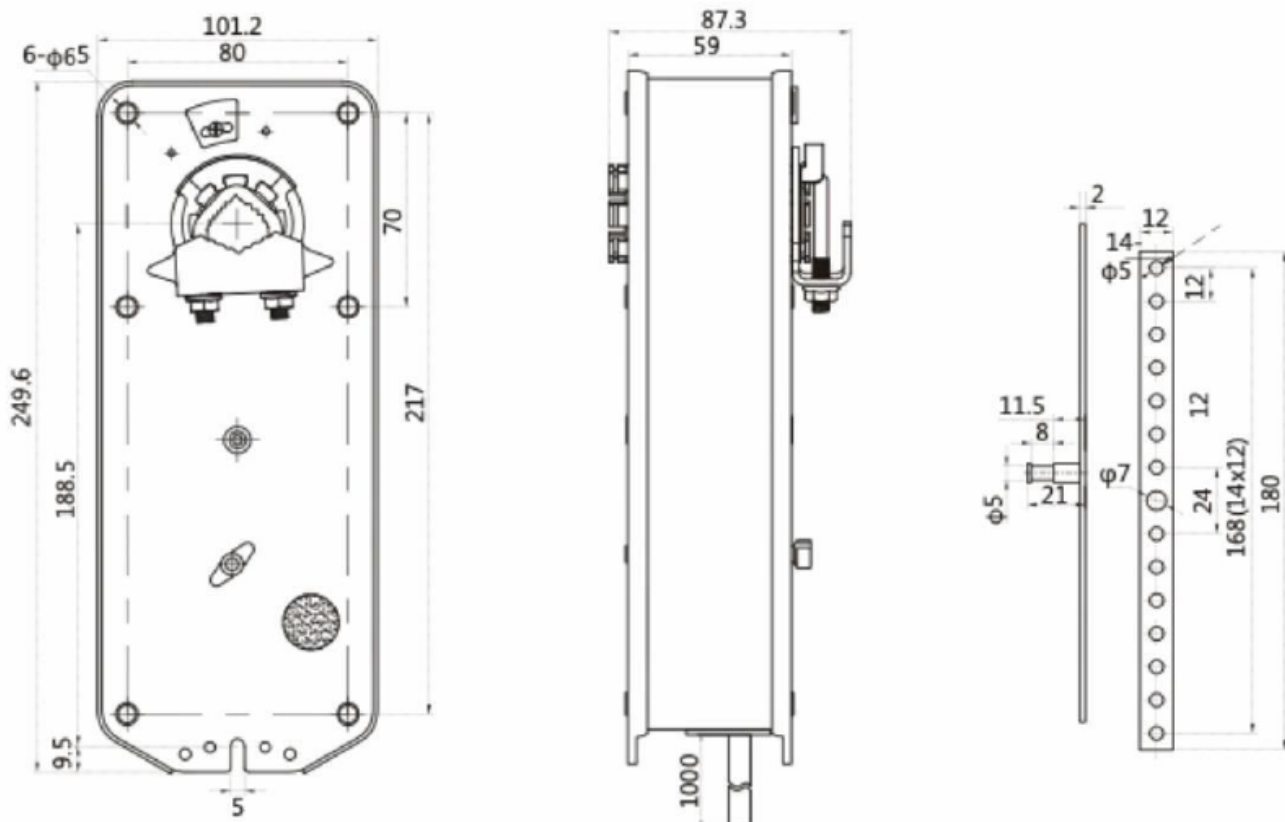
Общий вид и габаритные размеры электропривода VR15WS230-D(DS)
